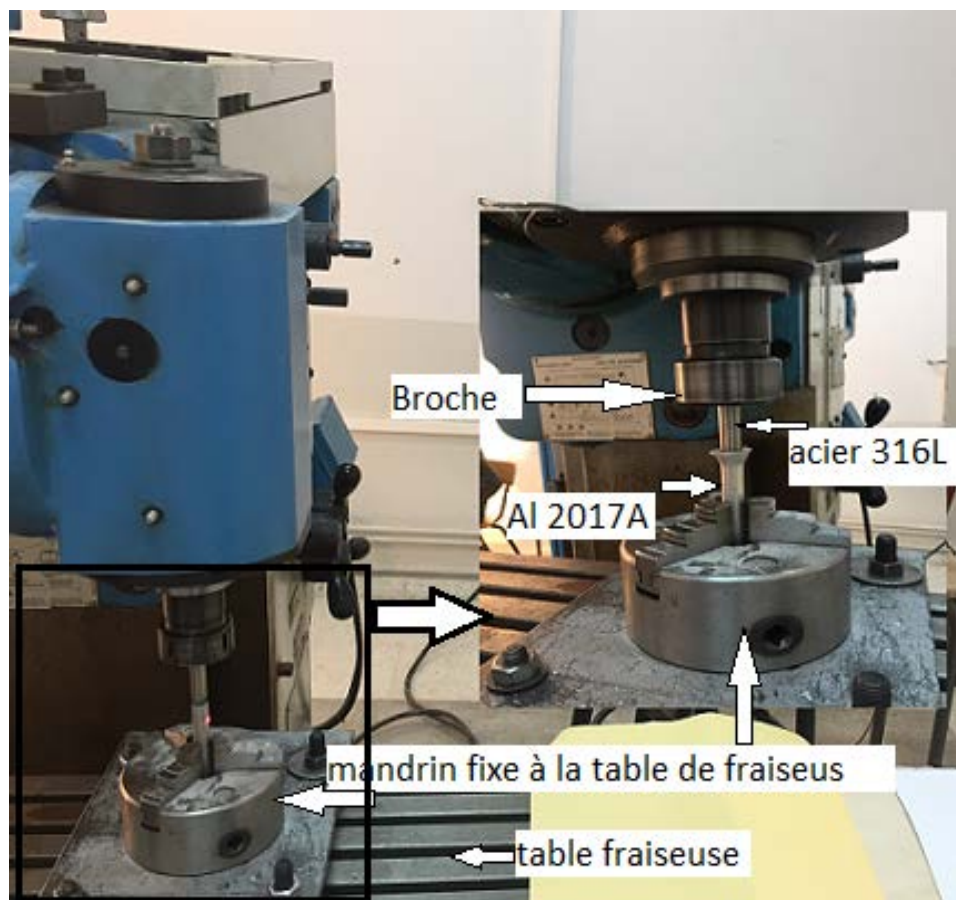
Vue du processus de soudage par friction rotative acier inoxydable AISI 316L – Alliage d'aluminium 2017A
